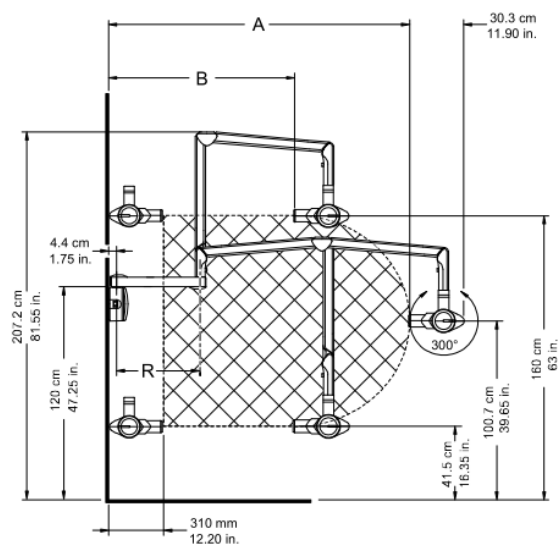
Aparat opcja z pionowo instalowaną płytą montażową
